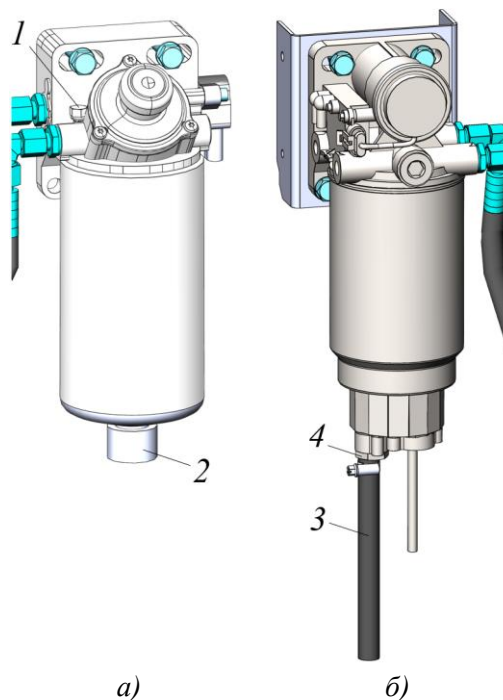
Фильтры грубой (предварительной) очистки топлива
